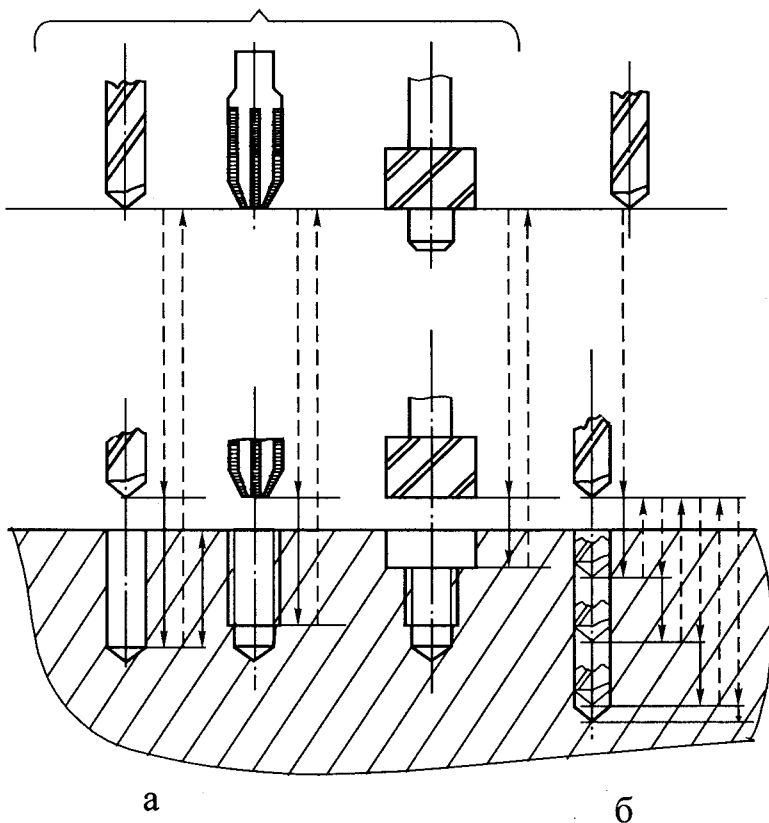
Стандартні цикли роботи багатоопераційного верстата.
